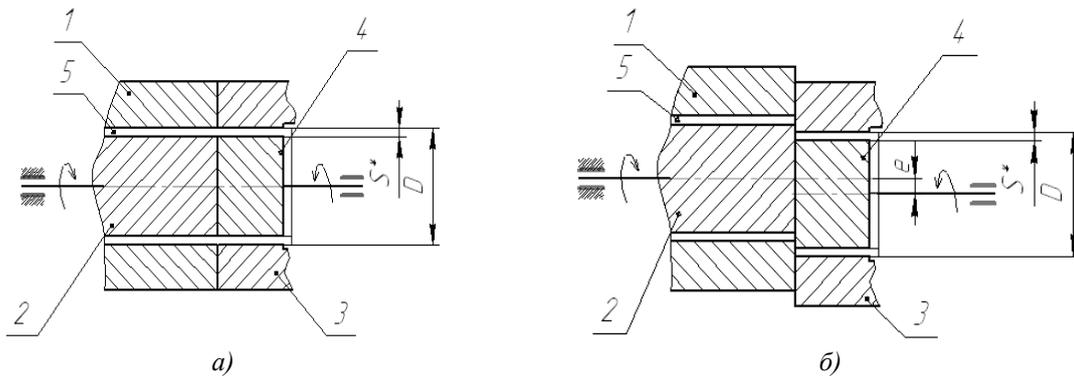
Схема устройства для резки труб одновременным сдвигом и кручением:
